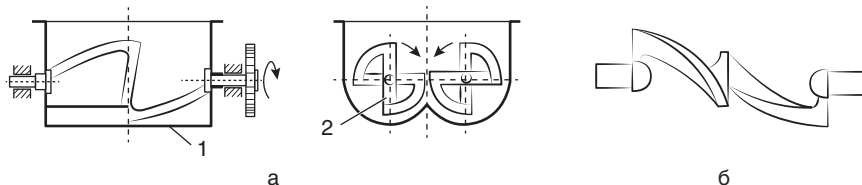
Смеситель с сигмообразными лопастями: а — общий вид; б — конструкция сигмообразных лопастей: 1 — корпус; 2 — вал
